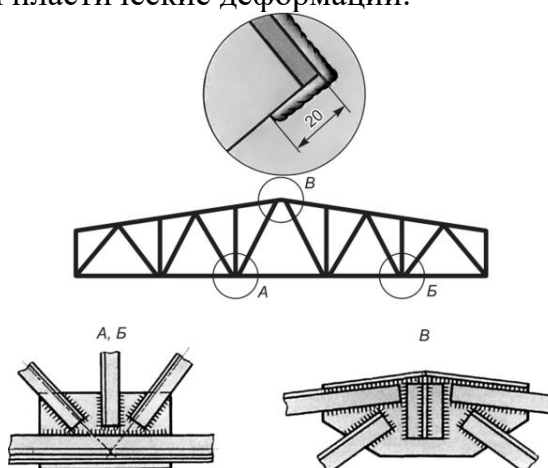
Сварка фермы и ее узлов А, Б, В
